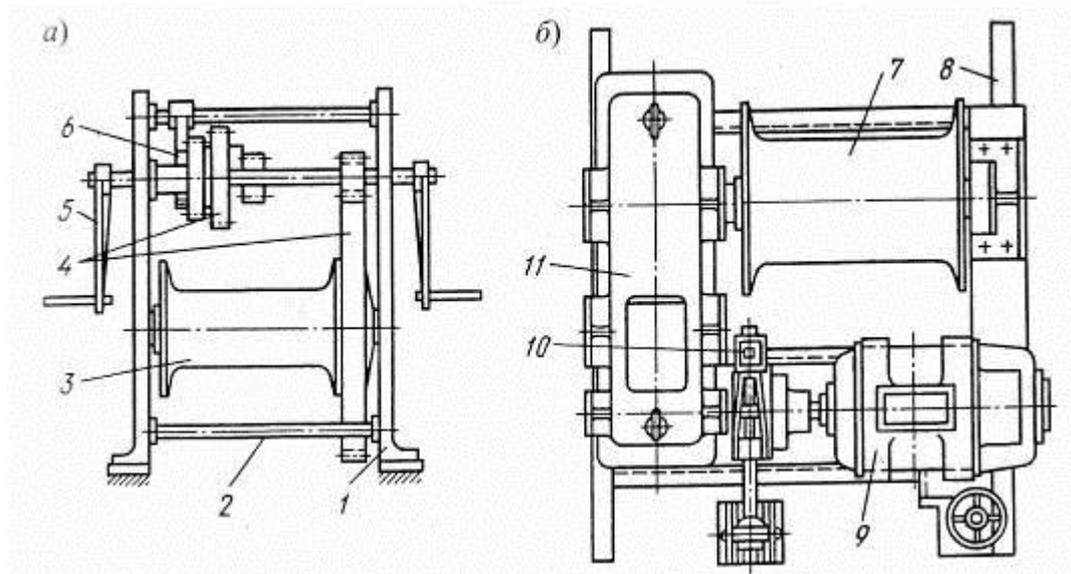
Лебедки: а — с ручным приводом; б — с механическим приводом; 1 — станина; 2 — тяга; 3, 7 — барабаны; 4 — зубчатая передача; 5 — рукоятка; 6 — храповой механизм; 8 — рама; 9 — электродвигатель; 10 — тормоз; 11 — редуктор
